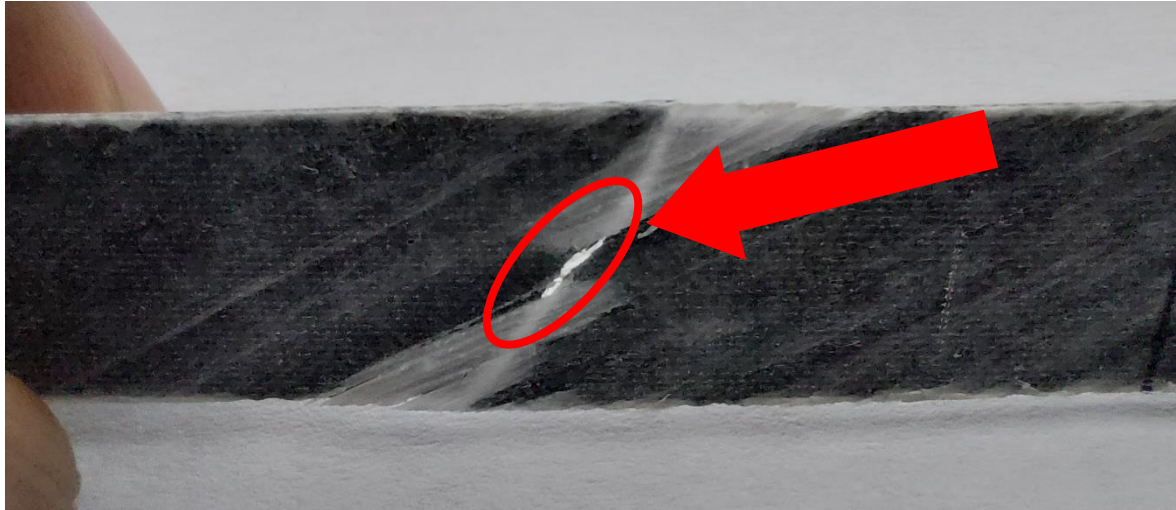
Fractura de la probeta FT5 del laminado [26/0₄/26].
